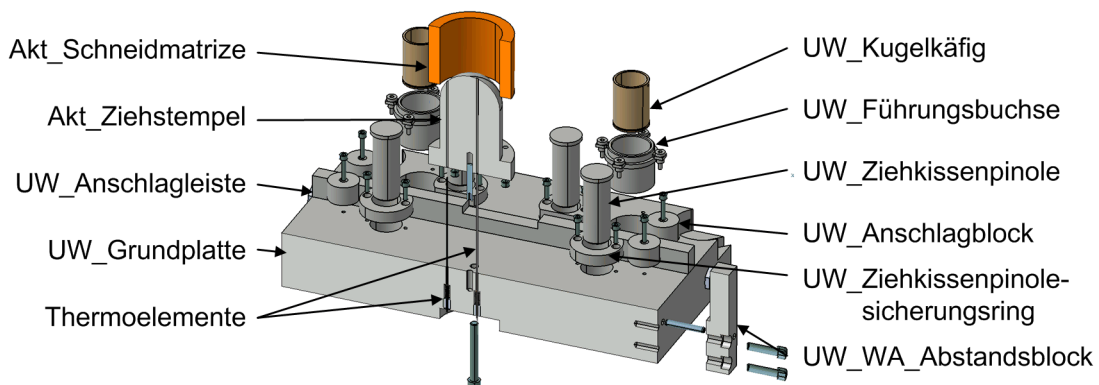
Untere Werkzeuggruppe (UW) des Halbwarmschneidwerkzeugs
